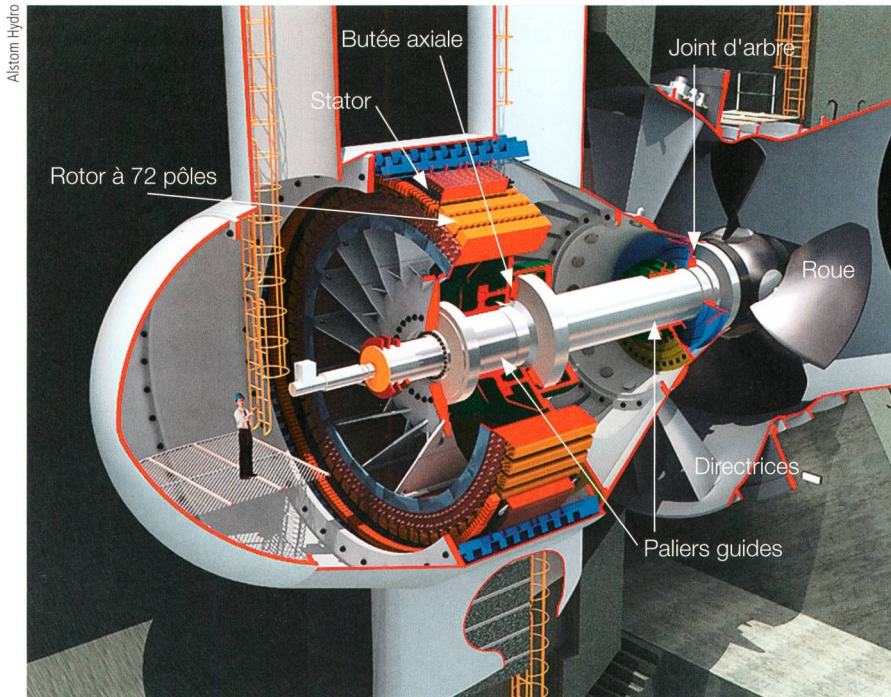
Vue éclatée d'un groupe bulbe (75 MW) de Santo Antônio montrant le générateur en puits (72 pôles, 100 min⁻¹), l'arbre supporté par les paliers guides, la butée axiale au niveau du générateur, les deux paliers guides et le joint d'arbre près de la roue, les directrices diagonales et la roue à 4 pales d'un diamètre de 7,5 m.
